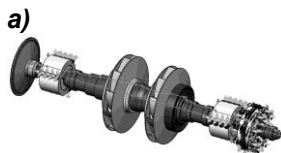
Ескіз ротора компресора агрегату для перекачки газу:
